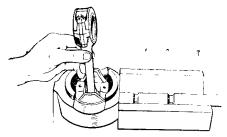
Приспособление для запрессовки поршневого пальца: 1 — направляющая; 2 — палец; 3 — плунжер
